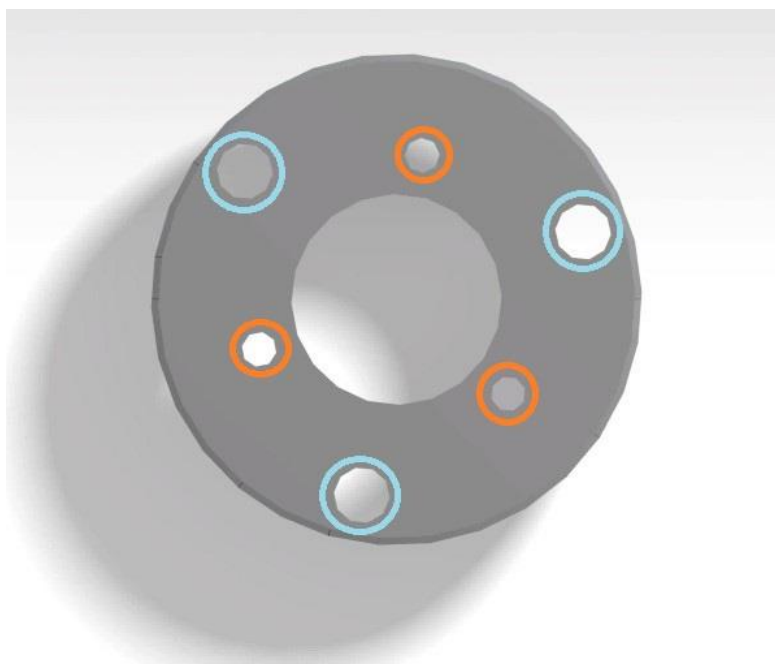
Vista en detalle del taladrado de la base (Fuente: elaboración propia)
